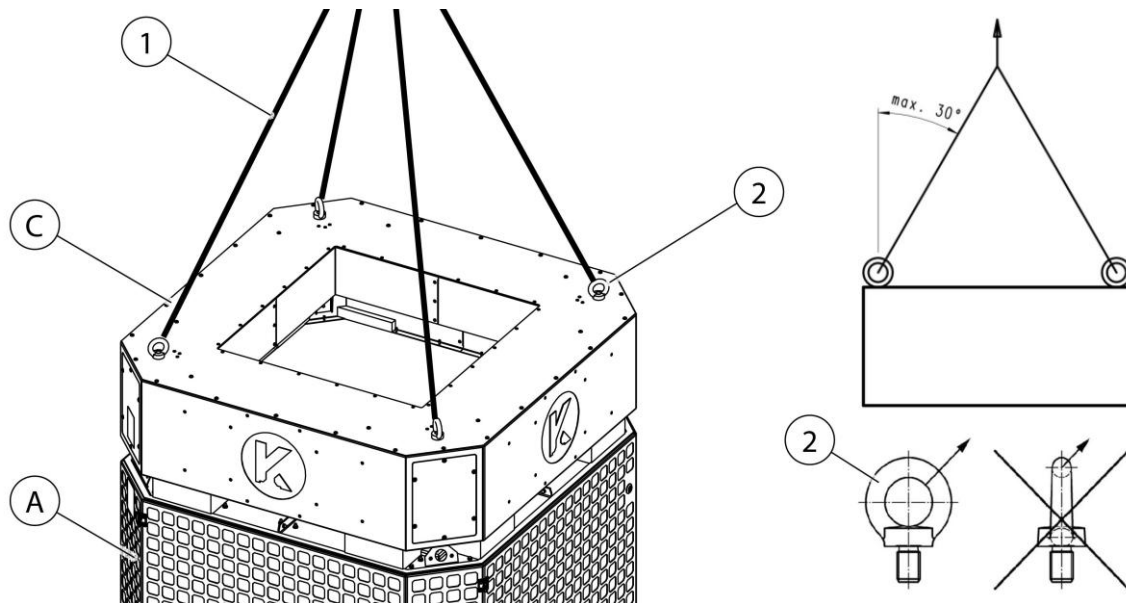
Heben des Produkts mit Kran/ Hebewerkzeug
